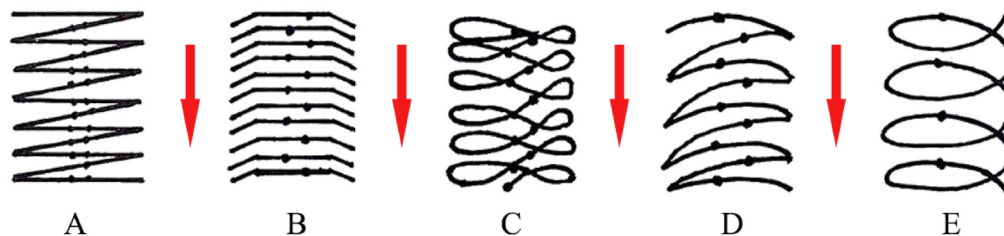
Movimientos para efectuar una soldadura ondeada
